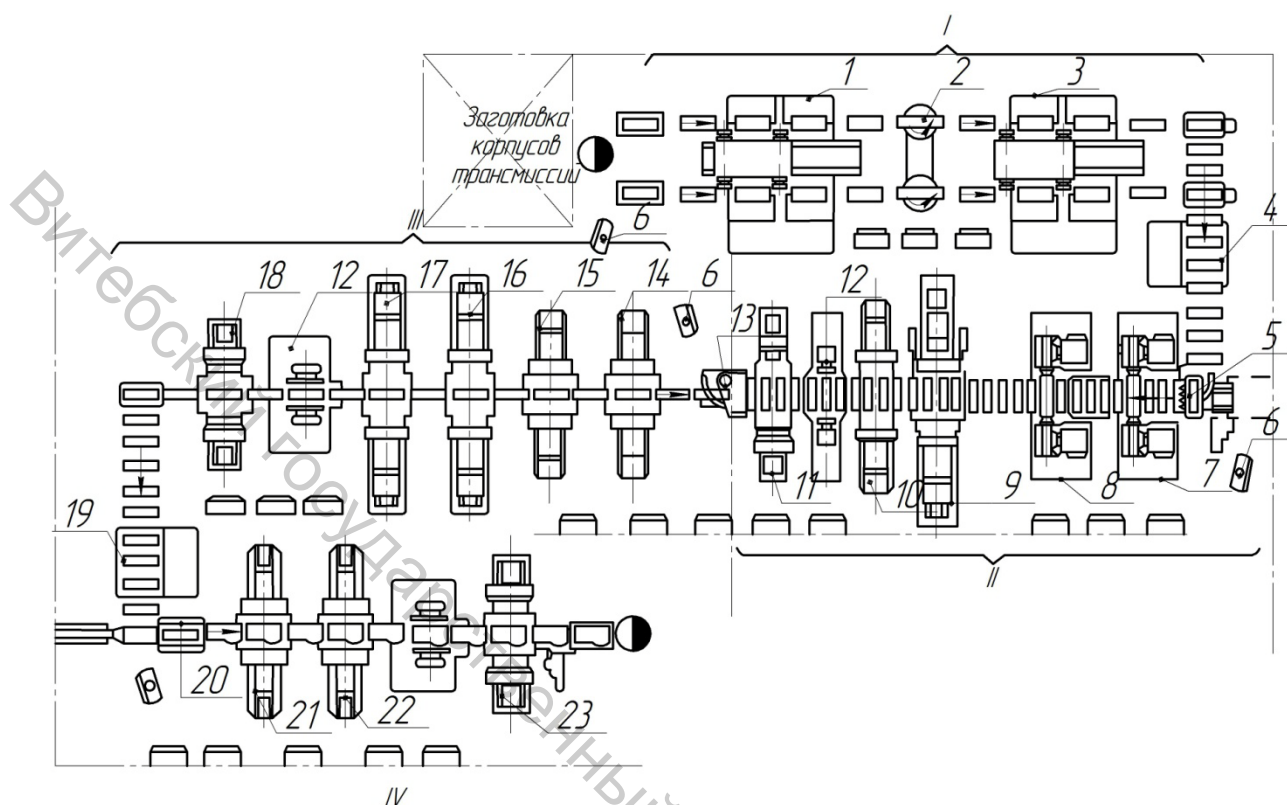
Схема автоматической линии для обработки корпуса трансмиссии трактора: 1,3,7,8 – фрезерные станки, 2, 5, 13 – поворотные столы; 4, 19 – поперечные транспортеры; 6 – пульт управления участками; 9,10 14, 15, 16, 17, 21, 22 – станки для обработки отверстий; 11, 18, 23 – резьбонарезные станки; 12 – контрольные приспособления; 20 – поворотный барабан
